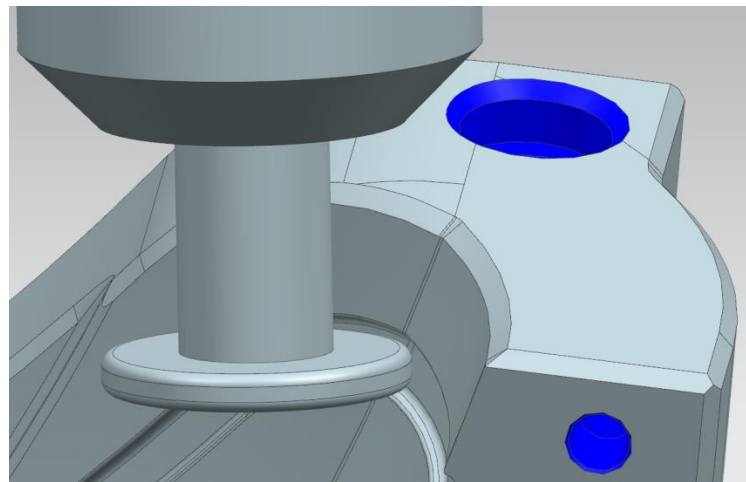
Schéma dráhy lemovací rolny v přípravku
